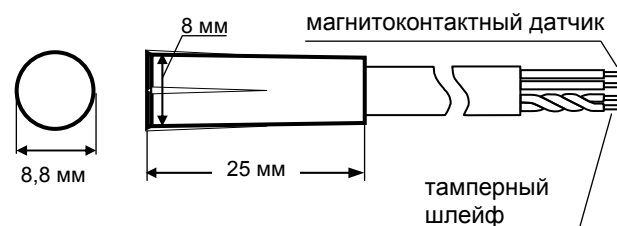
Геркон извещателя К-2 2Е в пластмассовом корпусе
